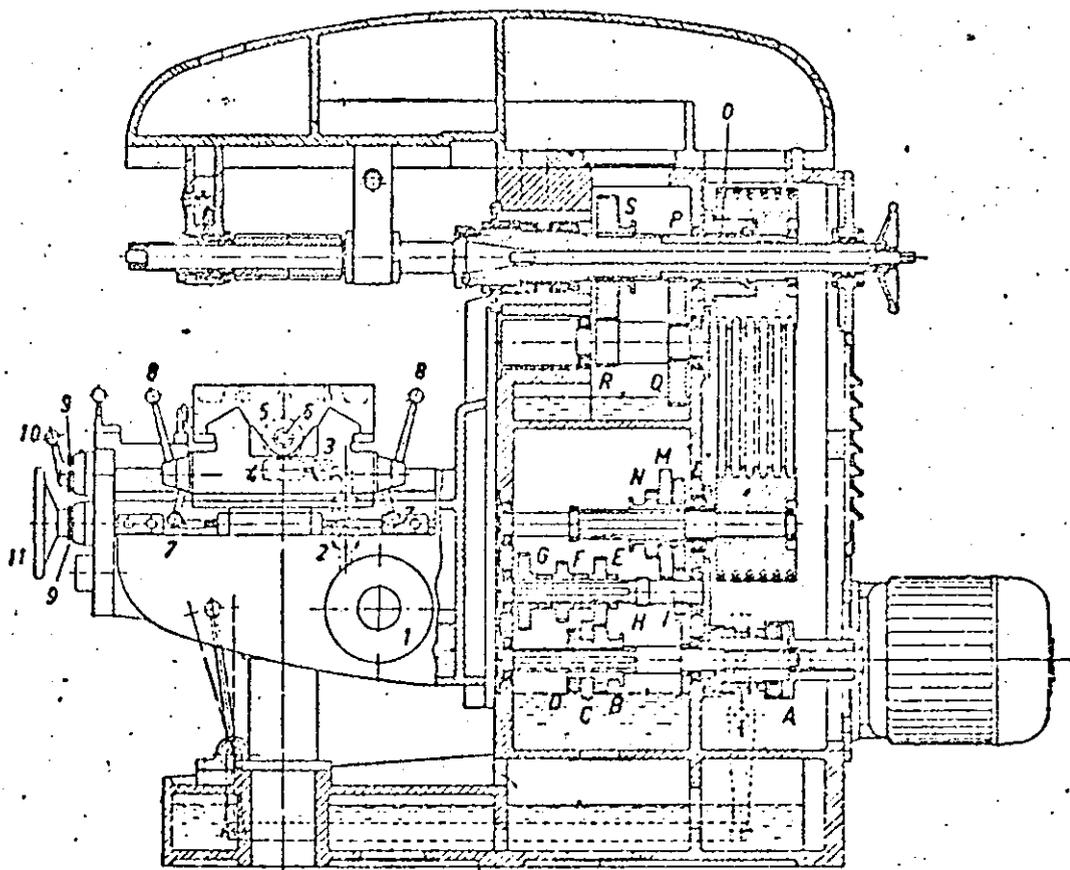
Seção duma fresadora horizontal. (Produção da Cia. Heller, Tipo FH 120, Nürtingen).
